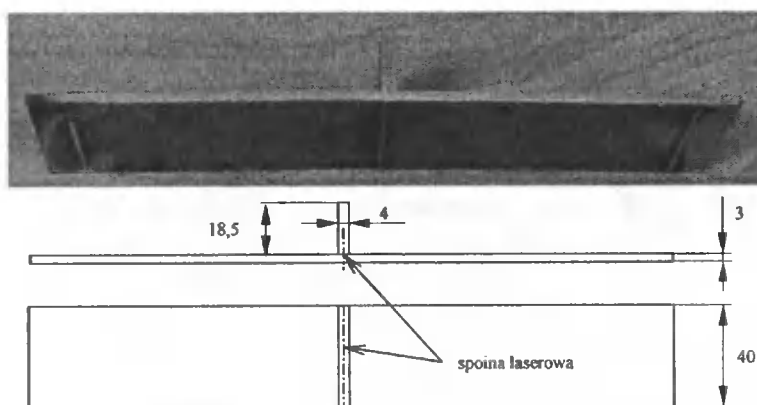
Stalowa struktura panelowa typu „sandwich” (firmy MW Niemcy) [7]
